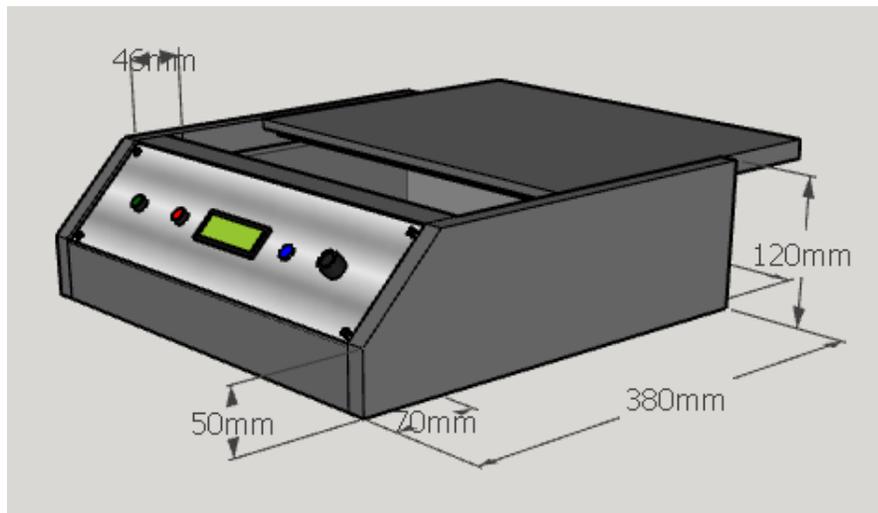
, 42 Diseño de prototipo de insoladora (dimensiones)
